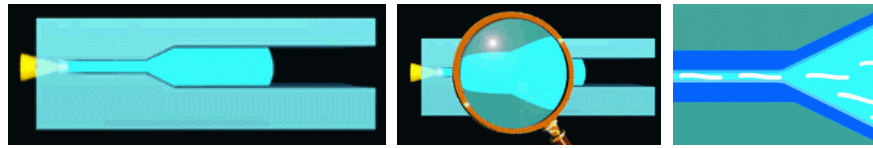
Llenado incompleto al solidificar la zona de entrada de material
